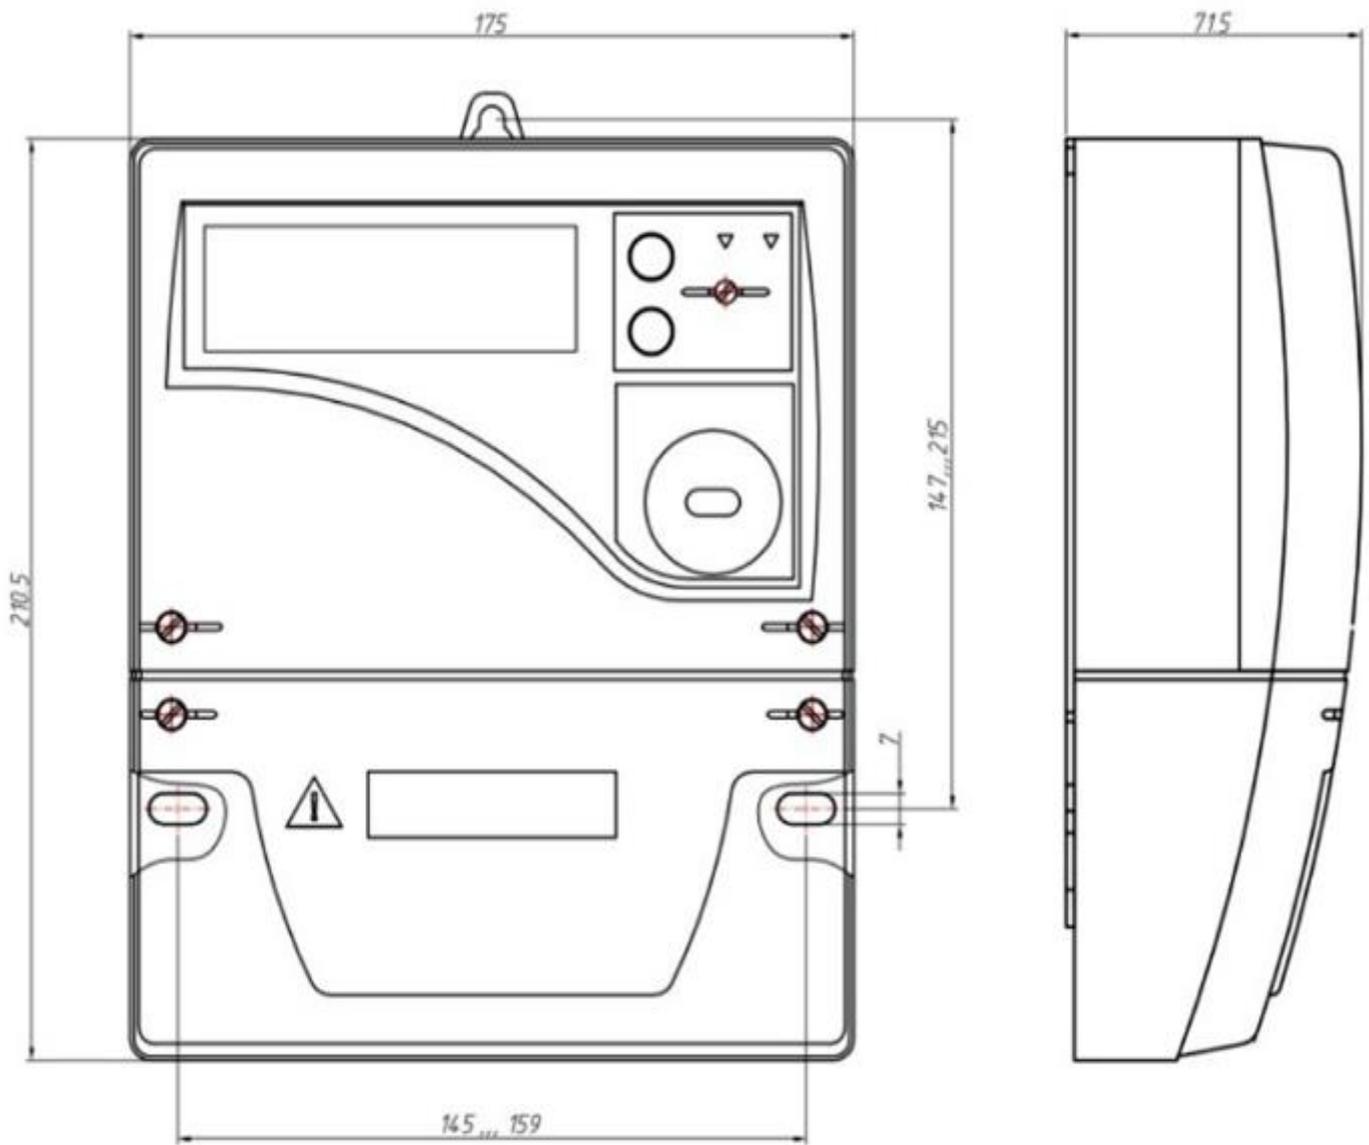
Габаритные размеры счетчика в корпусе «S31»
